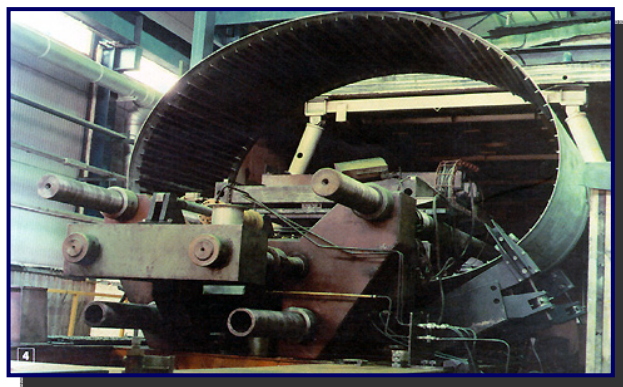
Сварная стрингерная оболочка в процессе изготовления
